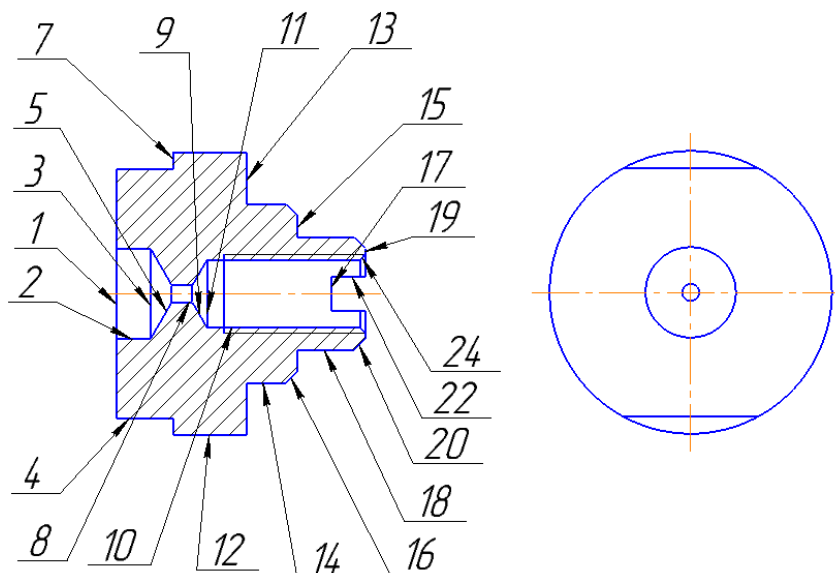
Обозначение обрабатываемых поверхностей детали
